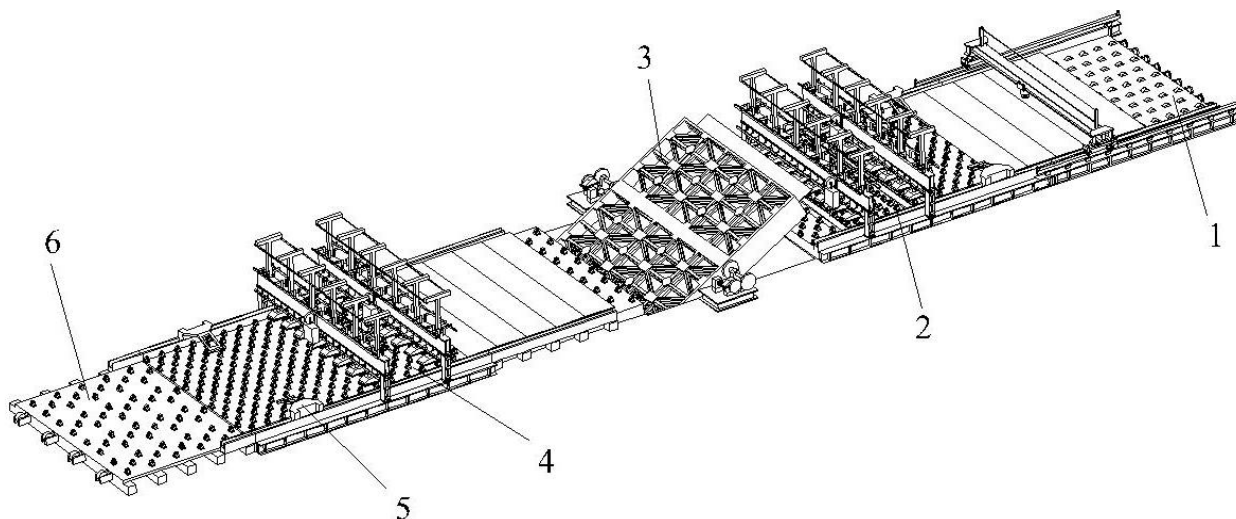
Линия сборки и сварки листовых полотнищ обечаек котлов железнодорожных вагонов-цистерн и контейнеров-цистерн:
